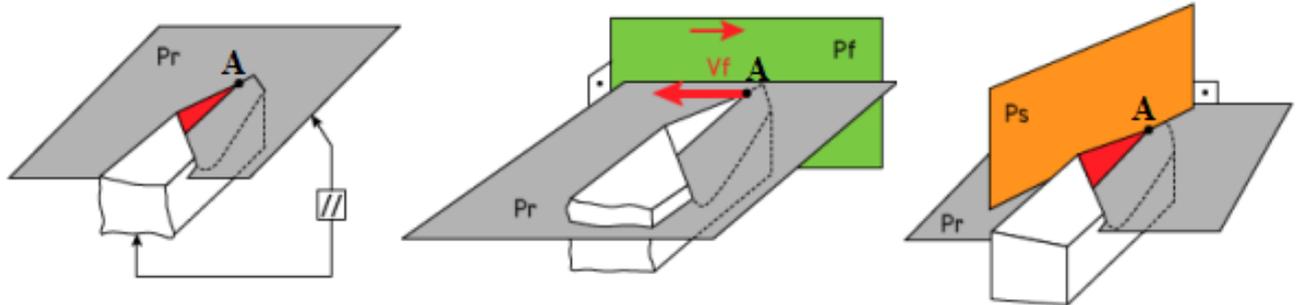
Plan de référence Pr , plan de travail conventionnel Pf , plan de l'arête de l'outil Ps .
